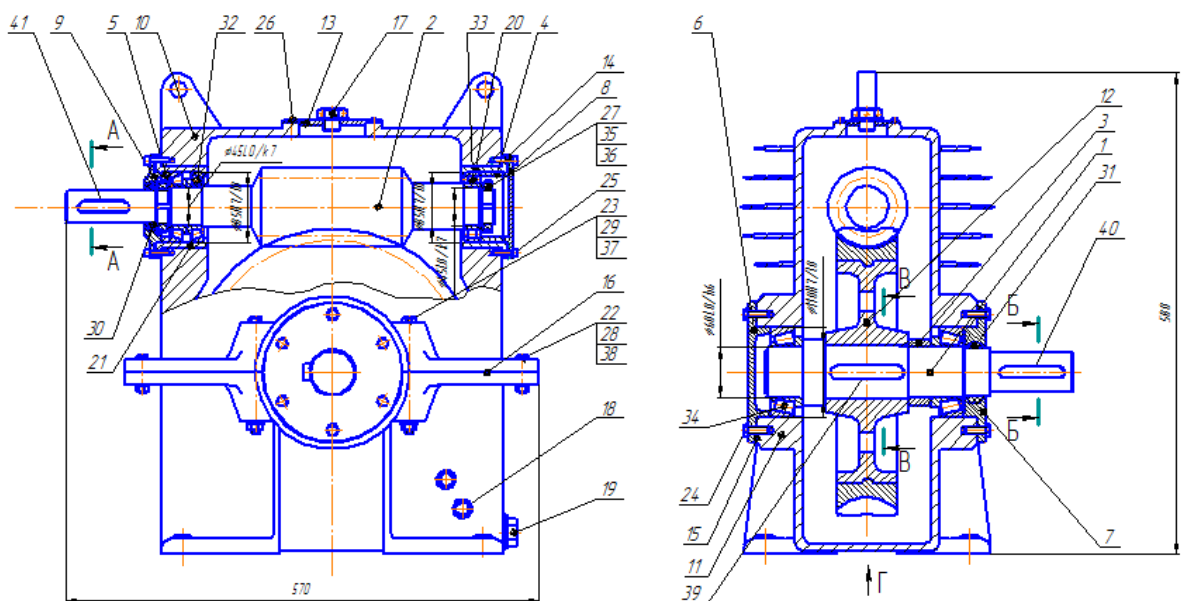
Редуктор черв'ячний РЧН-180М
